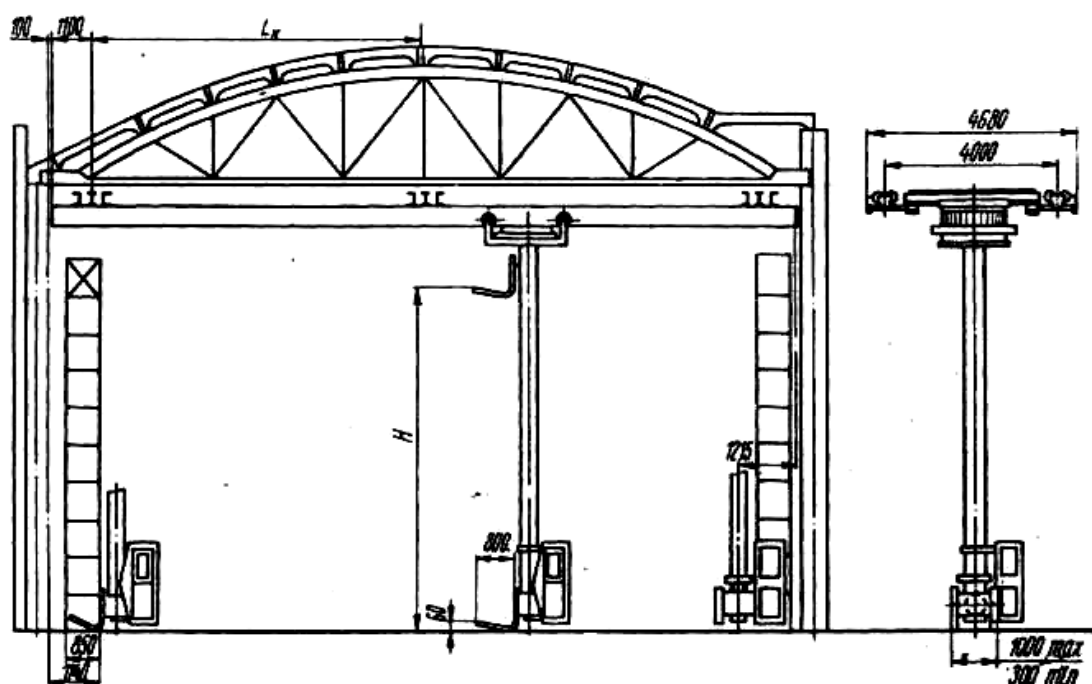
Кран-штабелер для укладки грузов в стеллаж или штабель
